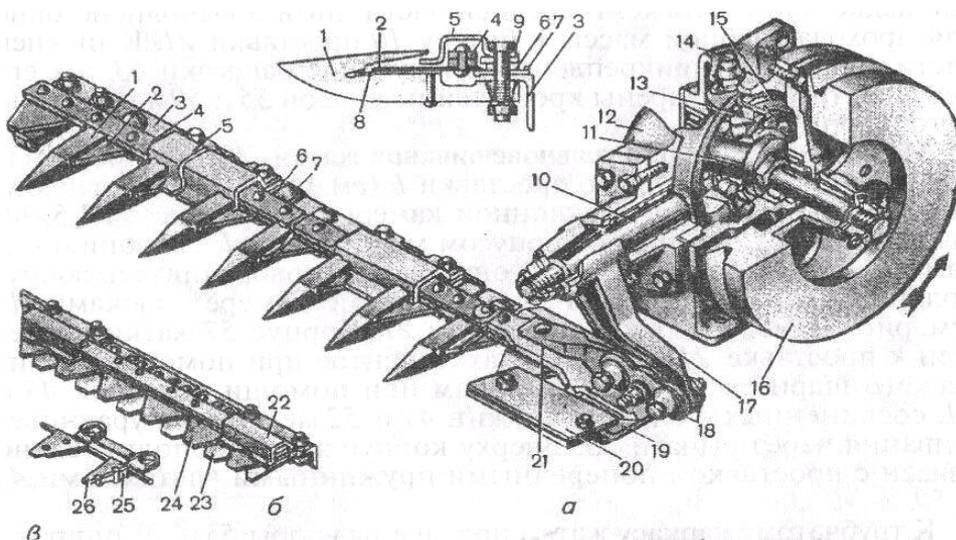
Режущий аппарат и механизм привода ножа комбайна «Дон»:
